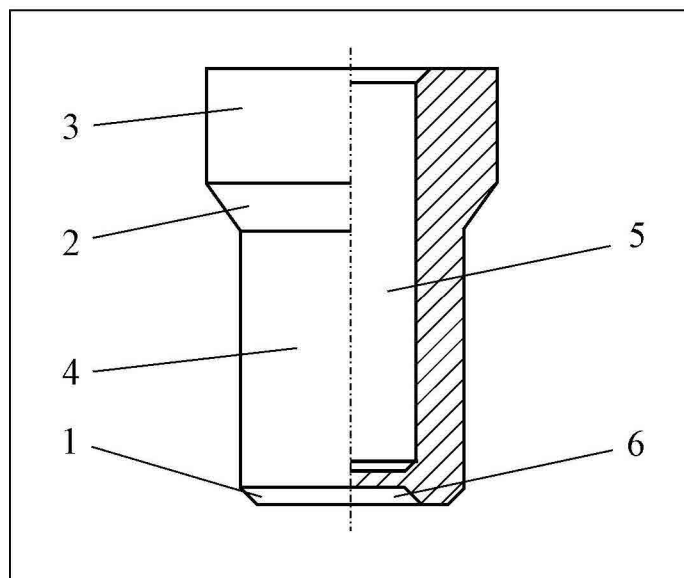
До розрахунку номінальної величини об'єму металу вихідної заготовки
